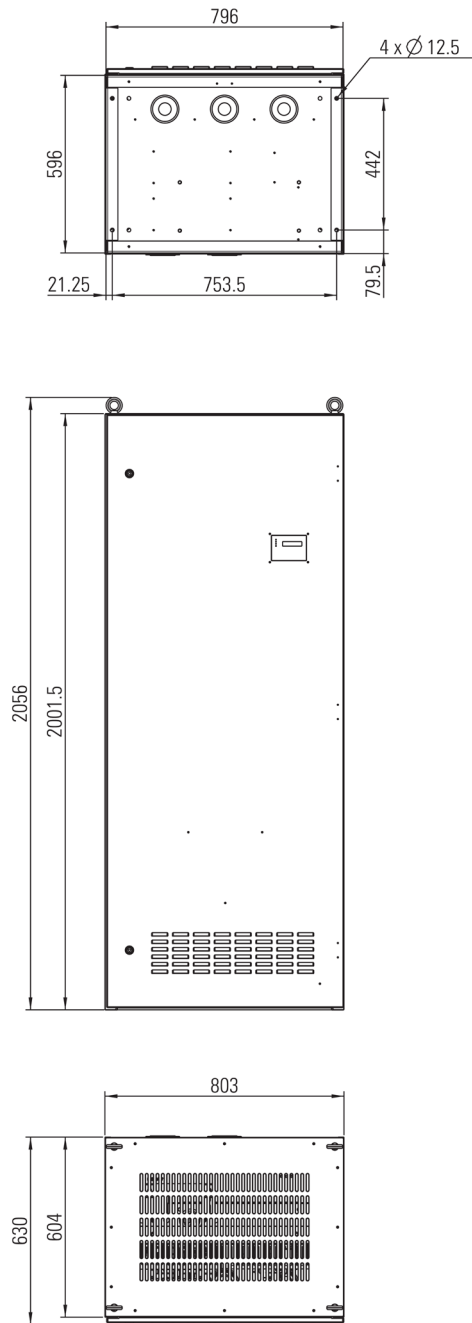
Dimensões do armário: 630 mm x 805 mm x 2115 mm.
